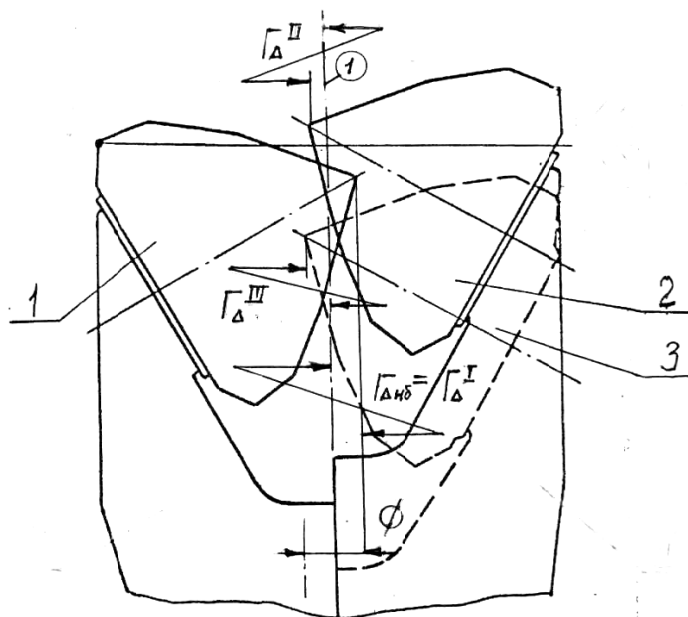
Схема смещений вершин конусов шарошек по разную сторону относительно оси базовой резьбовой поверхности долота:
